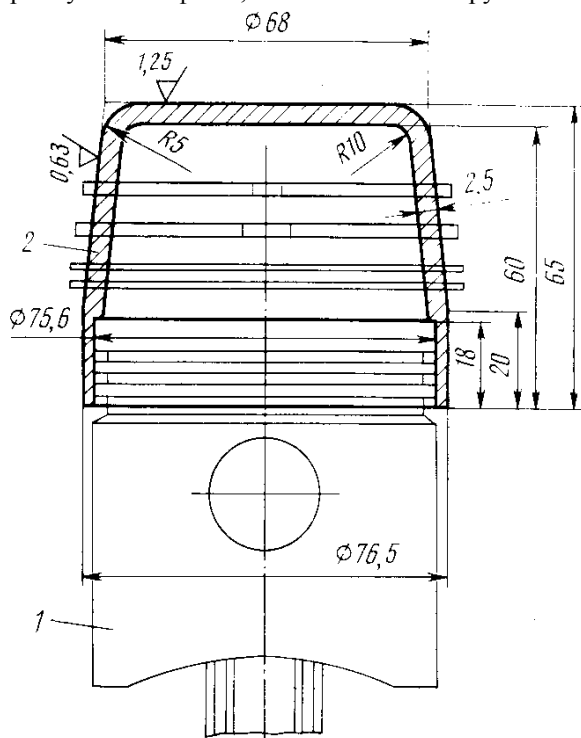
Оправка для установки на поршень поршневых колец: 1 — поршень; 2 — оправка
